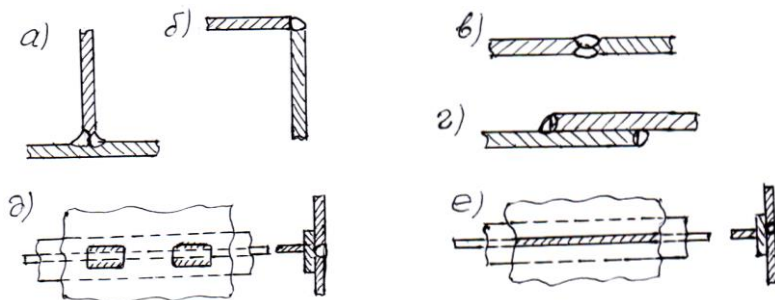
Виды сварных соединений деталей корпусных конструкций:
